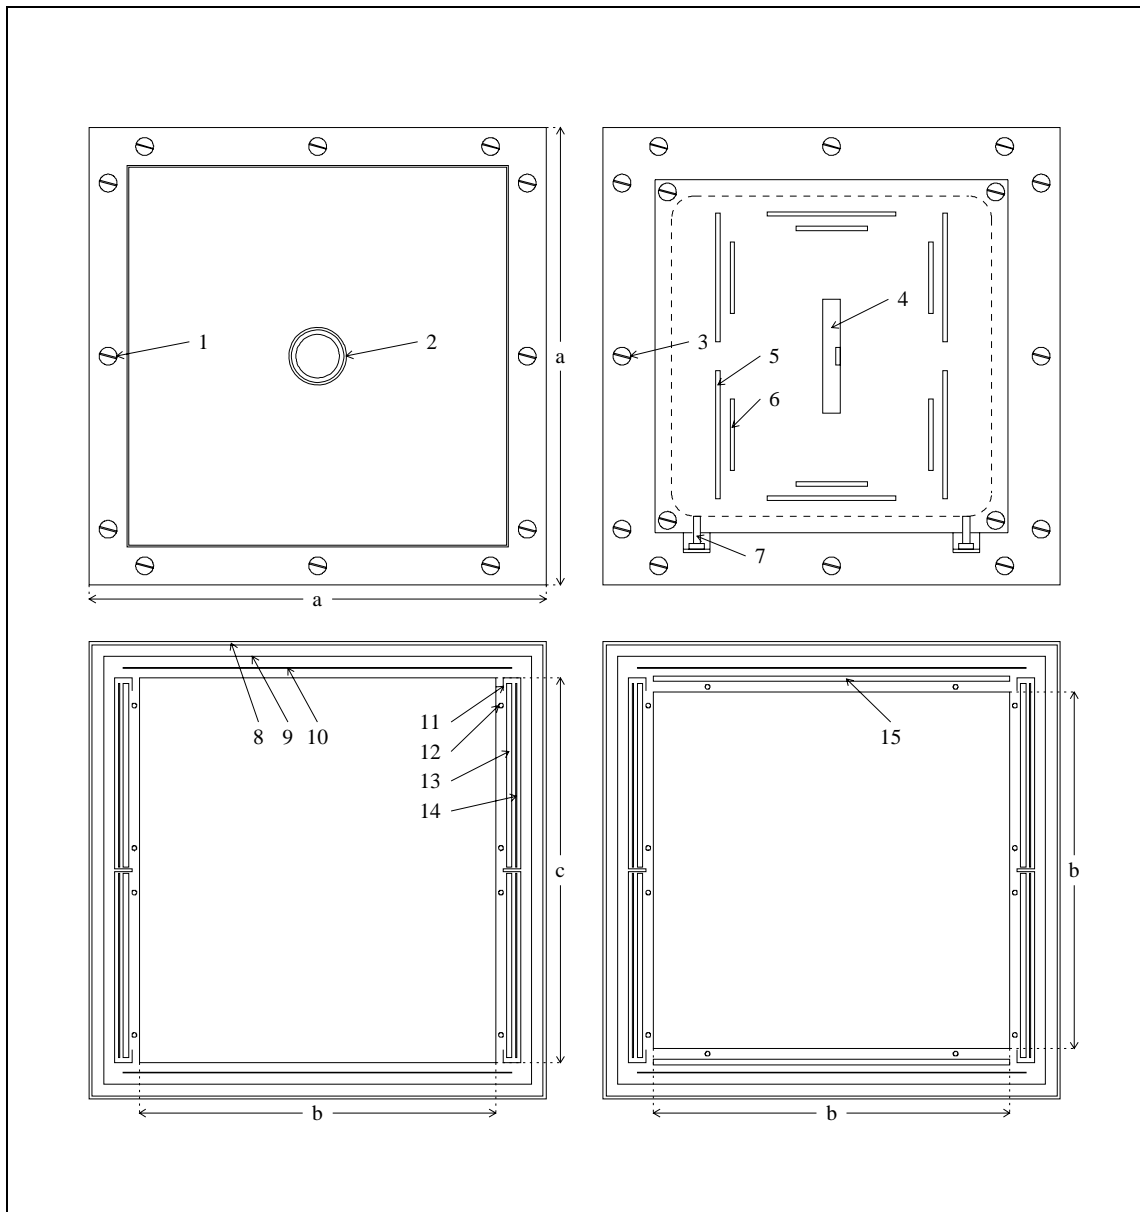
Aufbau der BEMC-Module - Front/Rückansicht/Querschnitt
